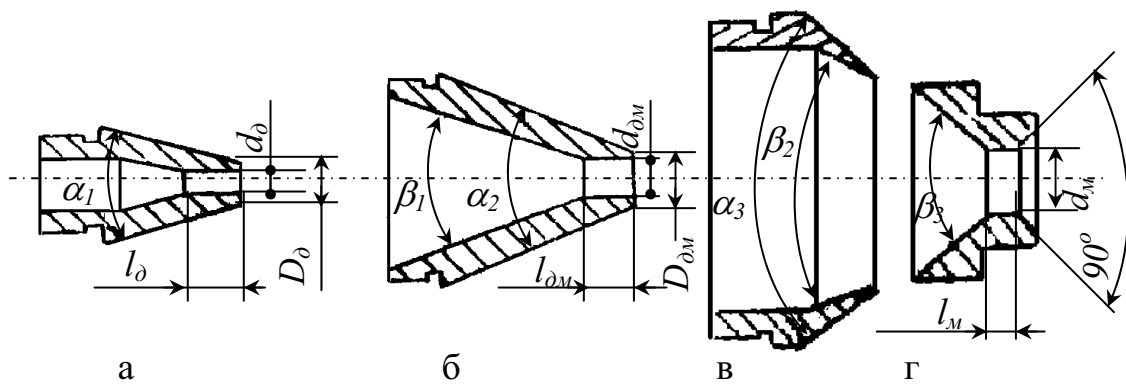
Формующий инструмент для трехслойного наложения изоляции и экрана: а – дорн; б – матрица-дорн 1; в – конус (матрица-дорн 2); г – матрица
